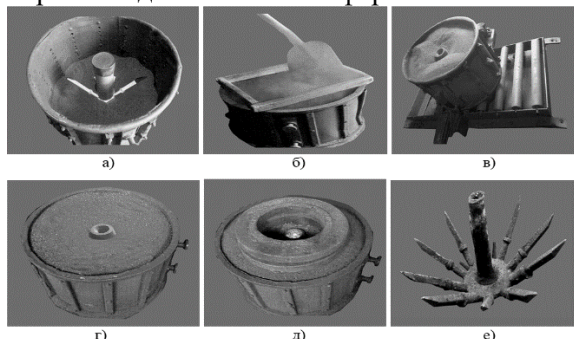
Процесс формовки и заполнения металлической опоки контейнера: а-формовка пеномоделей зубьев бороны; б-ручная формовка с кварцевым песком с помощью лопатки и сита; в-автоматическая вибрация; г-заполнение доверху; д-заливка расплава; е-стальные отливки деталей зубьев бороны с твердосплавным покрытием.
